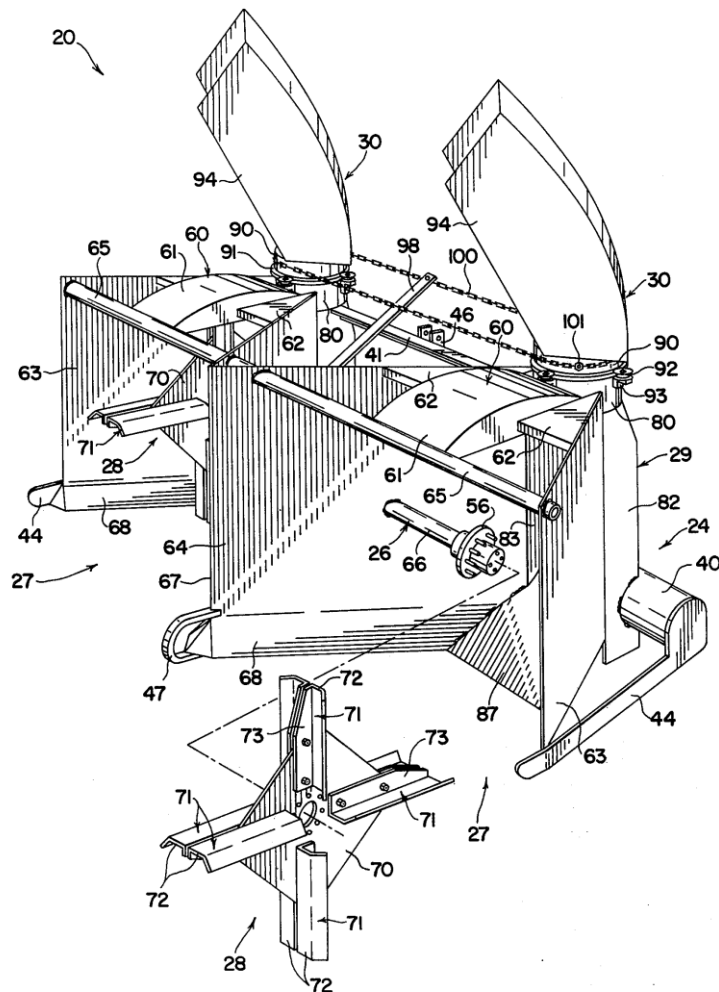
Общий вид дорожного снегоочистителя
